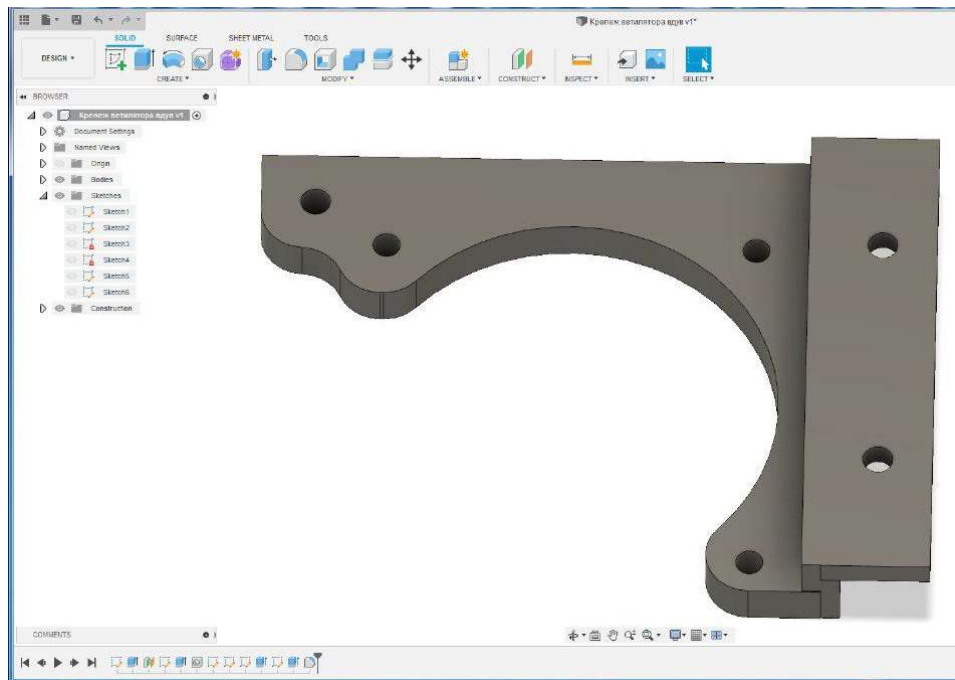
Кріплення вентилятора для виводу теплого повітря із корпусу принтера
